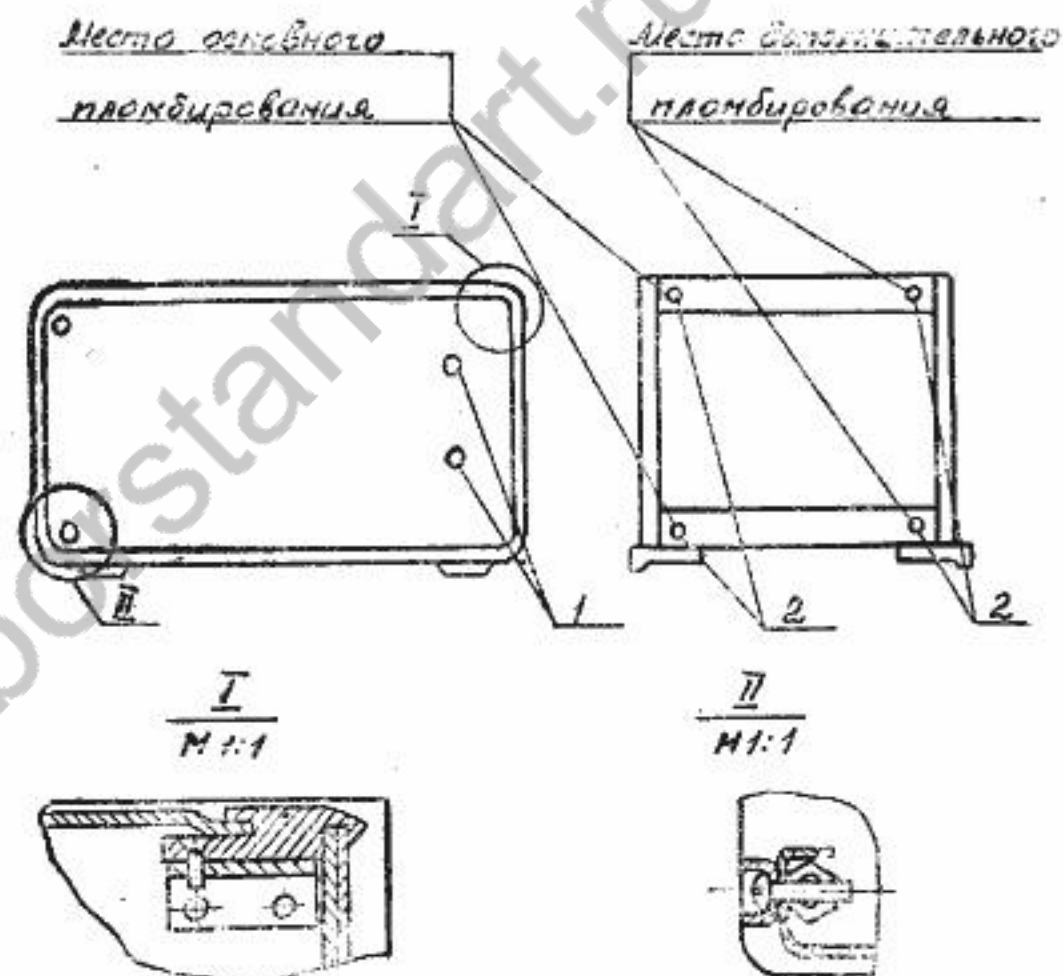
Крепление стенок, корпуса и расположение илэмб.
